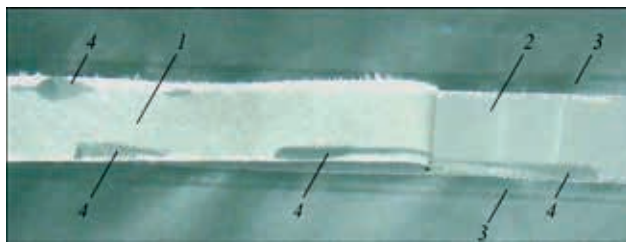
Зварний шов ламінованої тканини Unisol 950 з локальними непроварами по шву після випробування на відрив з'єднувальної стрічки: 1 – відірвана стрічка з оголеним кордом; 2 – зварний шов; 3 – зона термічного впливу біля шва; 4 – ділянки непровару на стрічці та на шві
